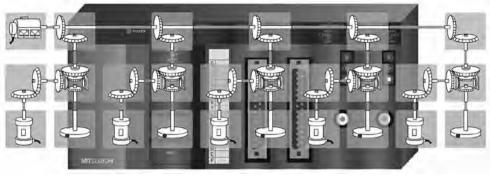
Виртуальная кинематическая схема зубообрабатывающего станка
